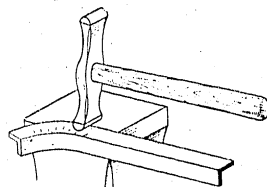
Schweißen eines Winkelprofils von Hand
